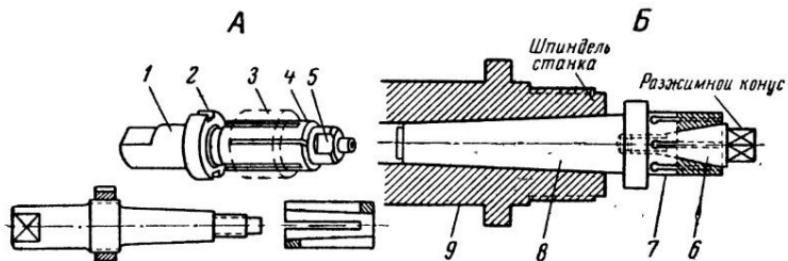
Разжимные оправки и их детали: А — центровая оправка (1 — тело оправки, 2 — гайка для съема обрабатываемых деталей, 3 — обрабатываемая деталь, 4 — разрезная втулка, 5 — гайка для разжима втулки); Б — шпиндельная оправка (6 — конус для разжима, 7 — разжимная часть — посадочное место для обрабатываемых деталей, 8 — хвостовик оправки, 9 — шпиндель станка).
